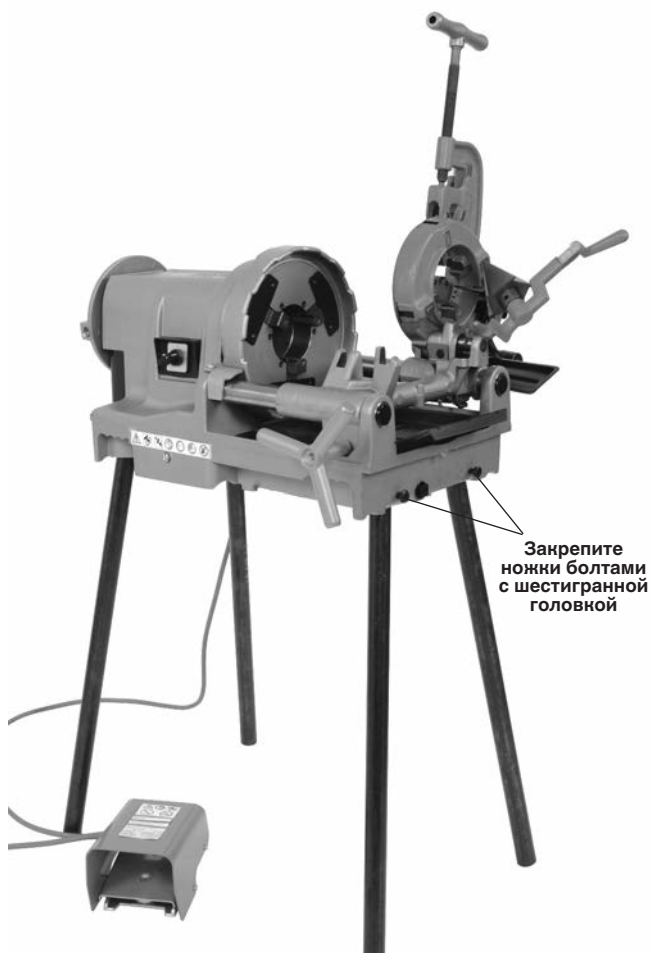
Установка резьбонарезного станка на трубные стойки
